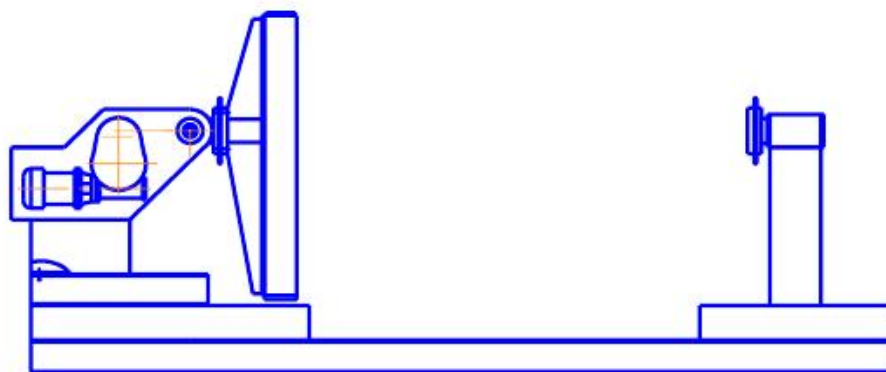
Конструктивная схема двухстоечного кантователя:
